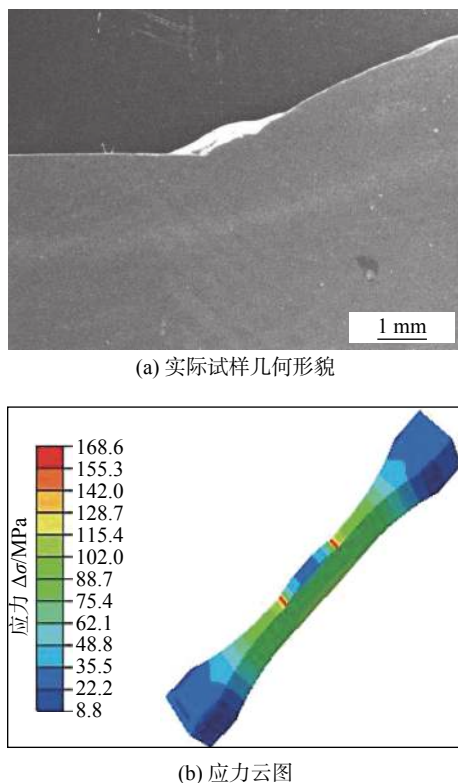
焊接接头焊趾处的几何形貌及主应力云图
